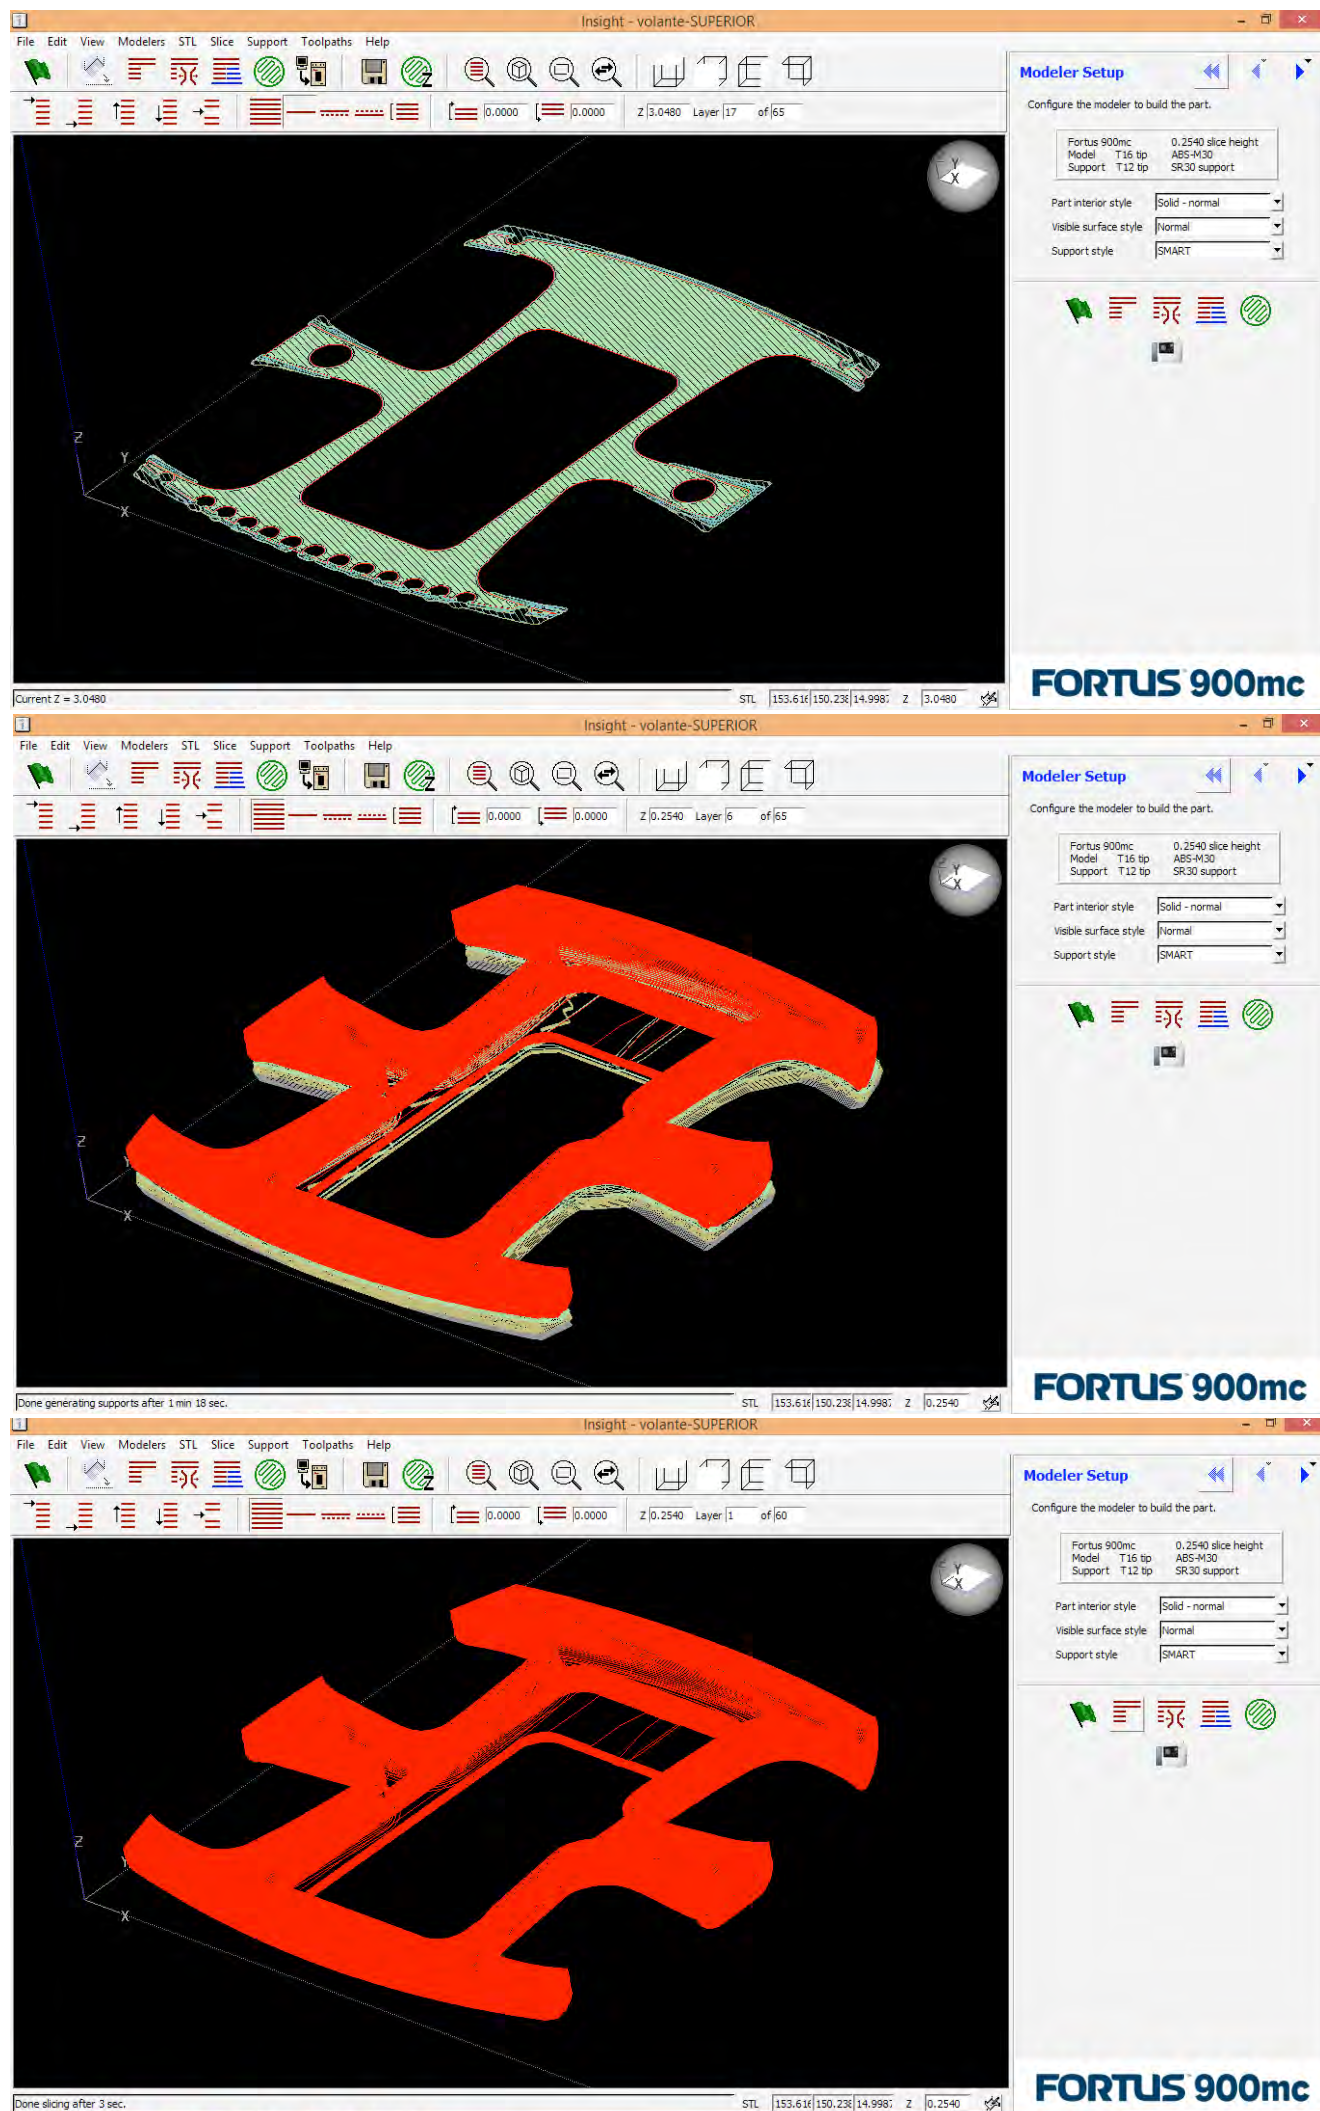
Proceso de impresión 3D de la parte superior del volante
